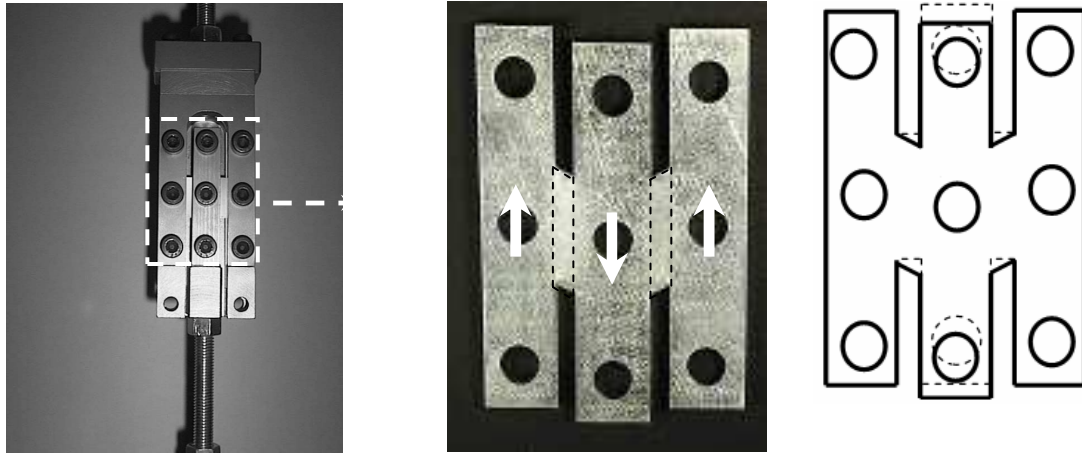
Dessin de définition d'une éprouvette Miyauchi.
